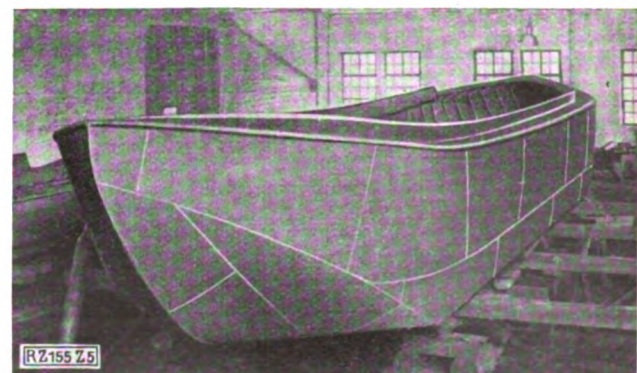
Außenansicht des fertig geschweißten Kähnes.
